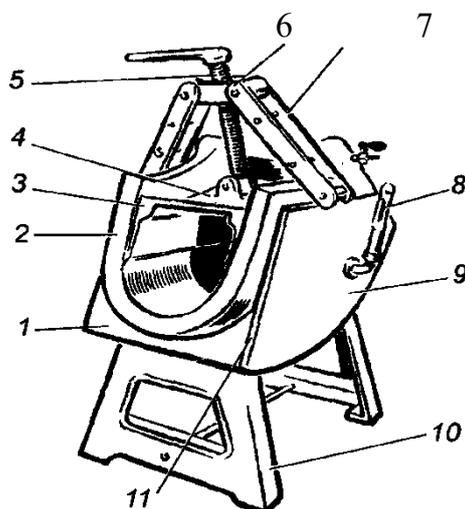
Секторная форма-мульда: 1 — корпус; 2 — паровая рубашка; 3 — бортовые вкладыши; 4 — подпятник; 5 — нажимный винт; 6 — траверса струбцины; 7 — струбцина; 8 — термометр; 9 — щиток; 10 — чугунная подставка; 11 — асбест для теплоизоляции корпуса мульды
